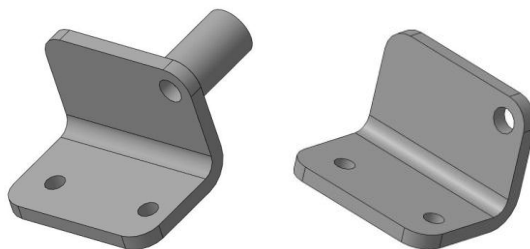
Изделие «Кронштейн поворотного механизма»
